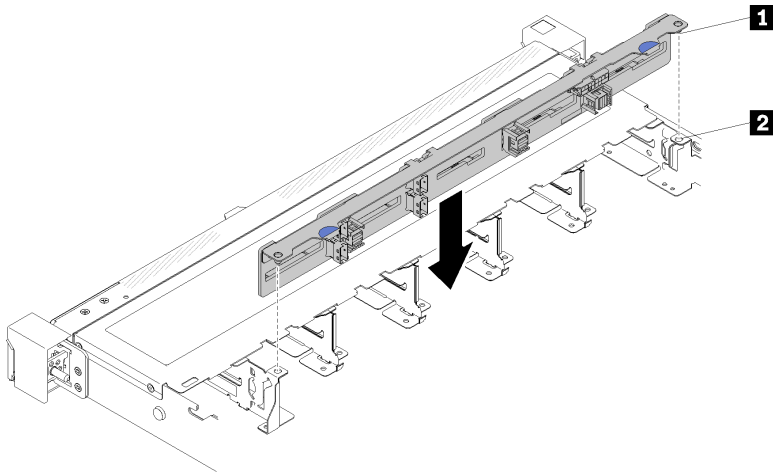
Installation d'un fond de panier d'unité 2,5 pouces remplaçable à chaud
